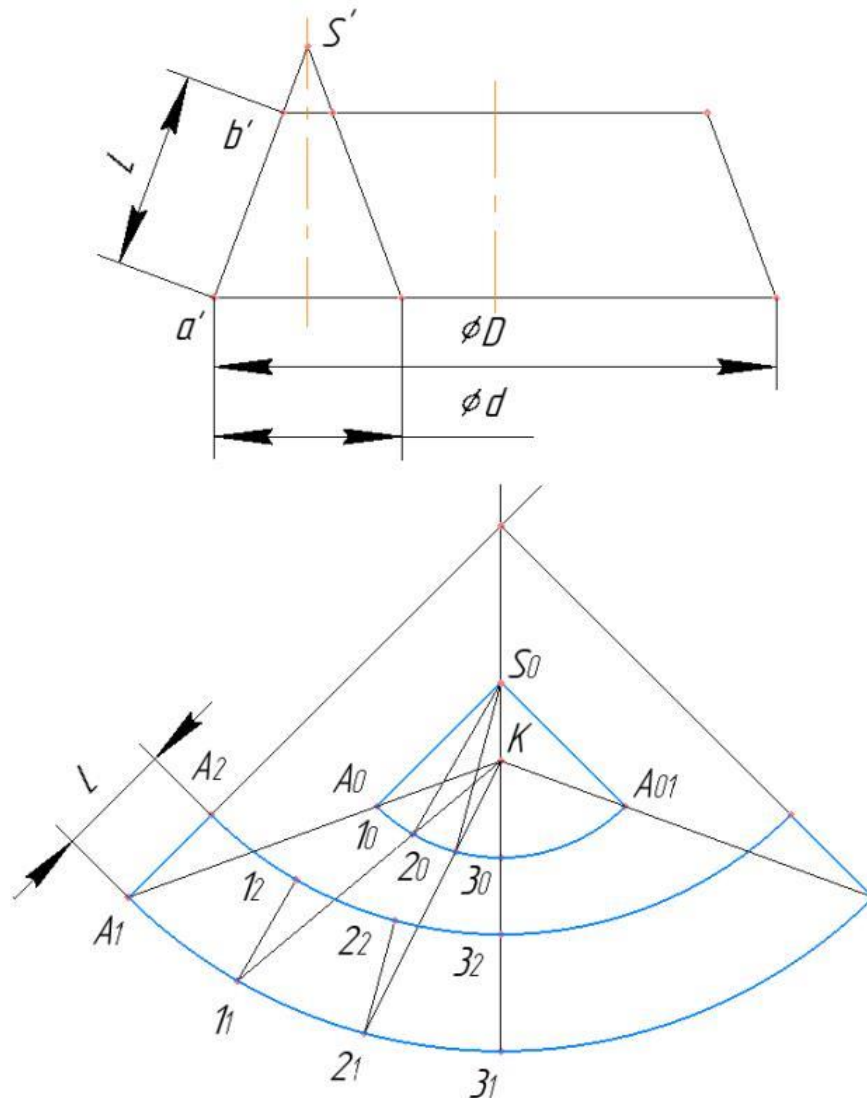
Развёртка конуса вращения с недоступной вершиной
